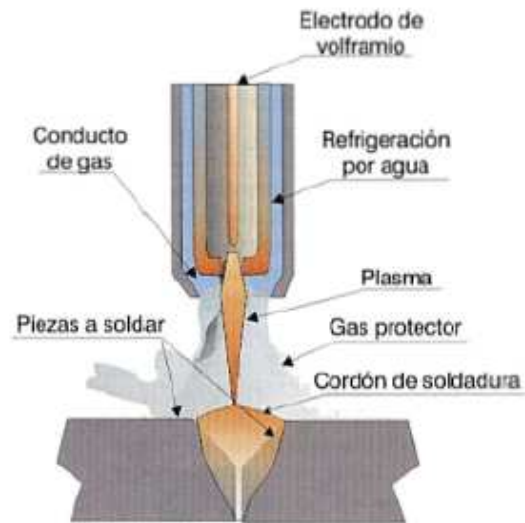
Equipo necesario para soldadura GTAW.
